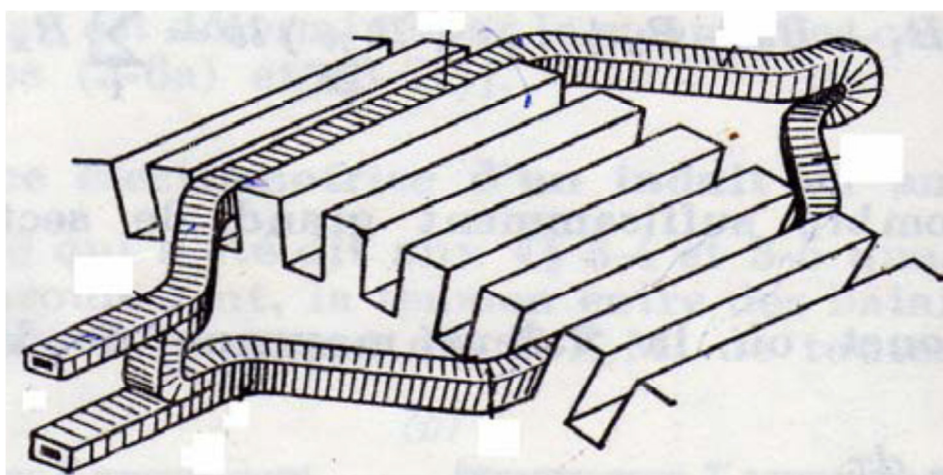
Disposition d'une section de l'enroulement d'un induit.
